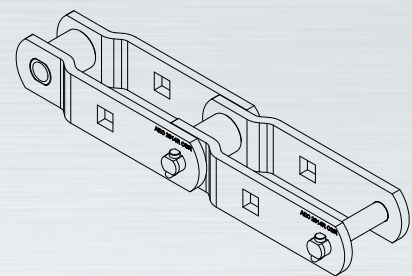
Cadena de placas acodadas para rodillos fuera de borda
